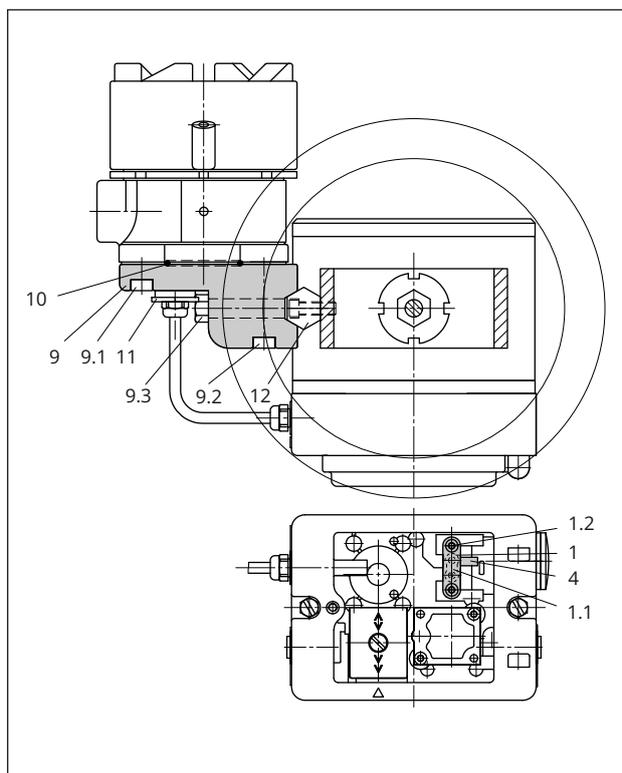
Anbau an Mikroventil mit Stellungsregler Typ 3760 ·
